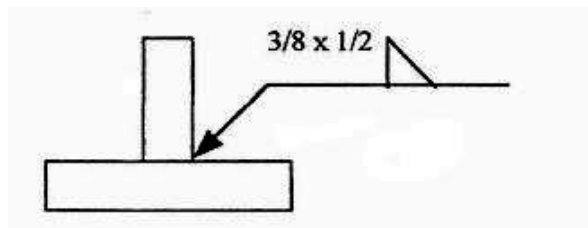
SOLDADURA DE FILETE CON PIERNAS DESIGUALES POR EL OTRO LADO DE LA FLECHA.
